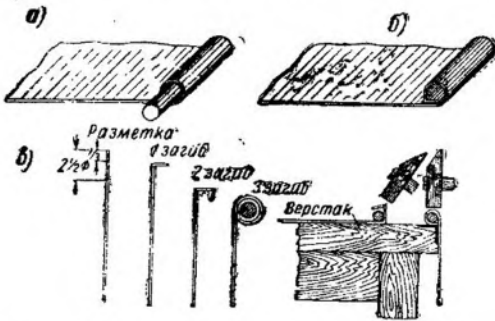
Ручная закатка проволоки в прямолинейной кромке
